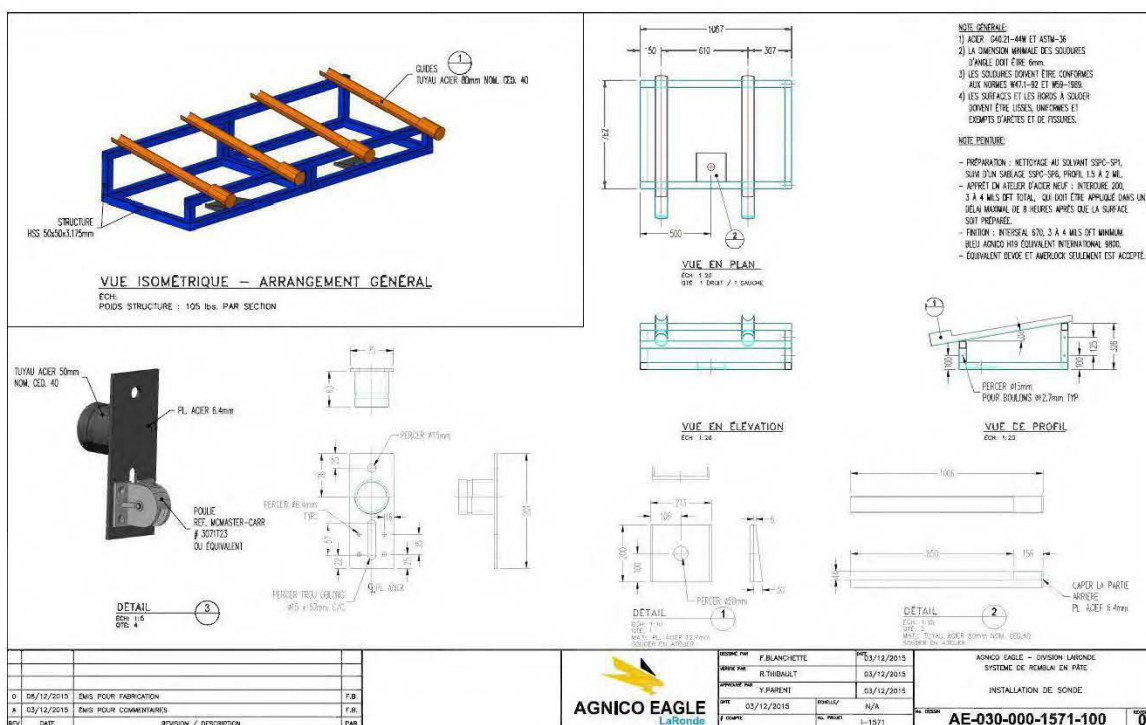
Dessin technique du prototype servant à insérer des tubes de forage et à attacher les cages à partir du plancher après le sautage de production.
